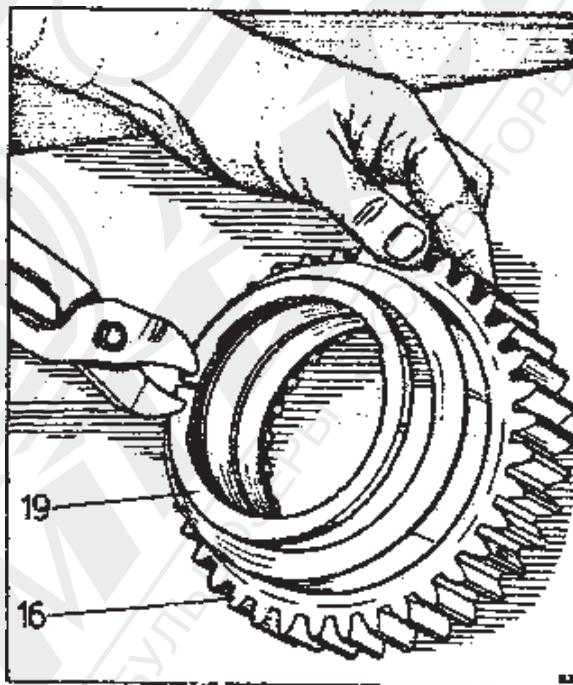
Установка пружинного установочного кольца 110w /19/ в крайнем канале зубчатого колеса 16
